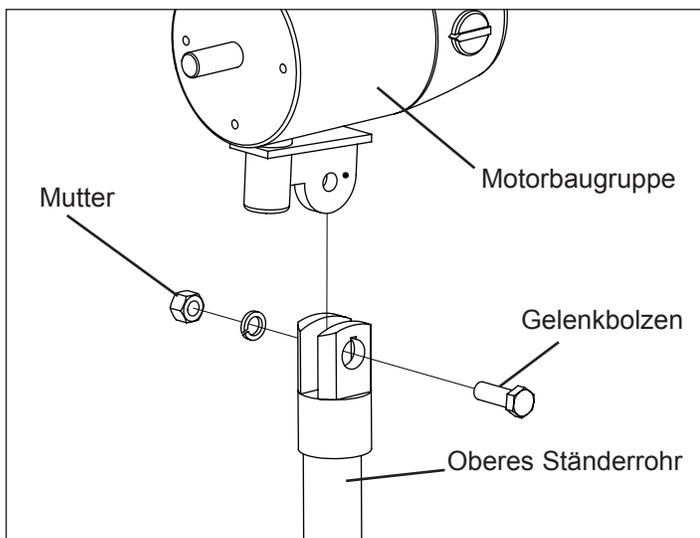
Motor an der Motorträgerbaugruppe befestigen
